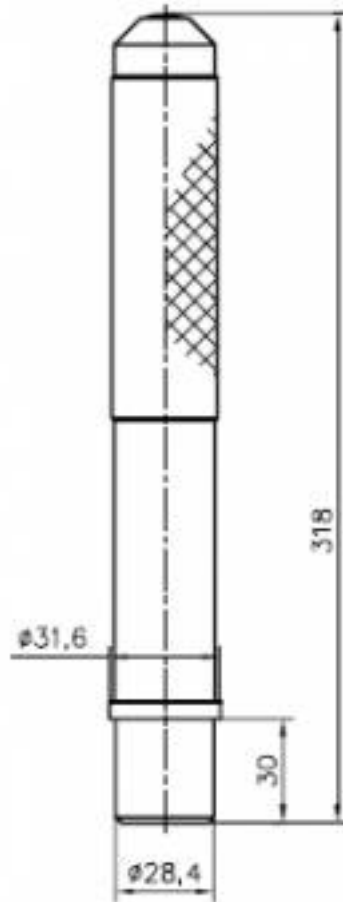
Оправка А.74105 для замены вала сошки картера рулевого механизма
